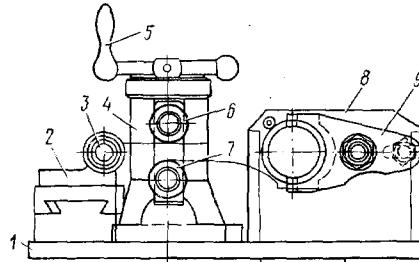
Приспособление для растачивания нижней и верхней головок шатуна:
